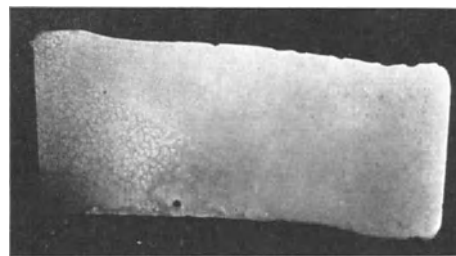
Gute Warschweißprobe im Schnitt (0,87 fache Vergrößerung).
